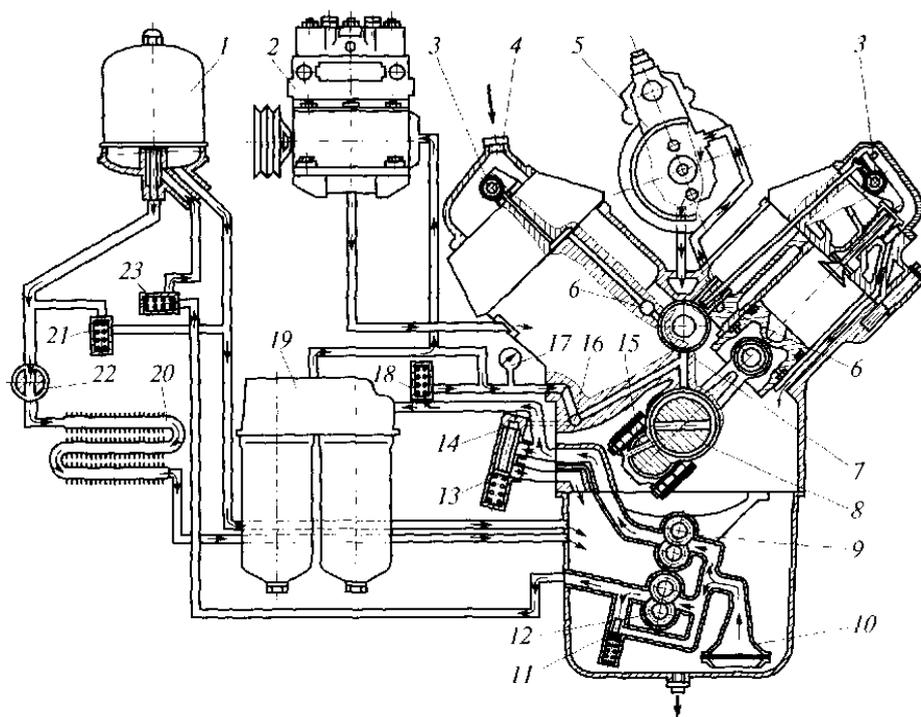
Схема смазочной системы двигателя автомобиля ЗИЛ-433100
